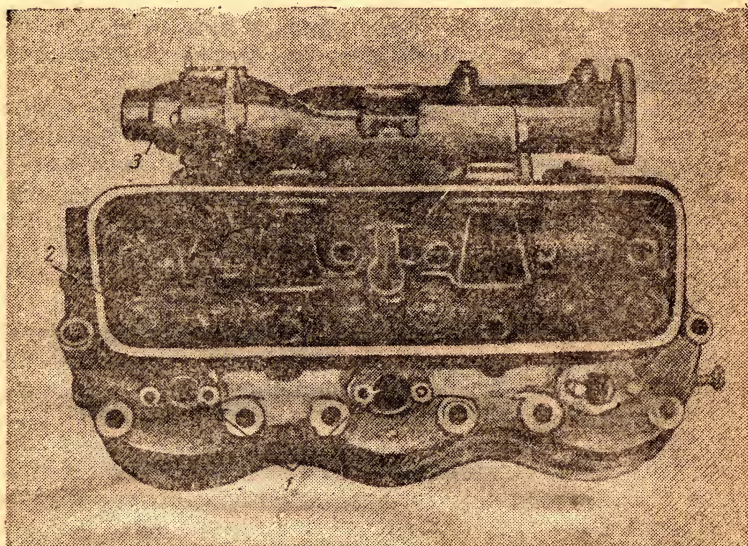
Головка цилиндров 6-цилиндрового V-образного дизельного двигателя:
